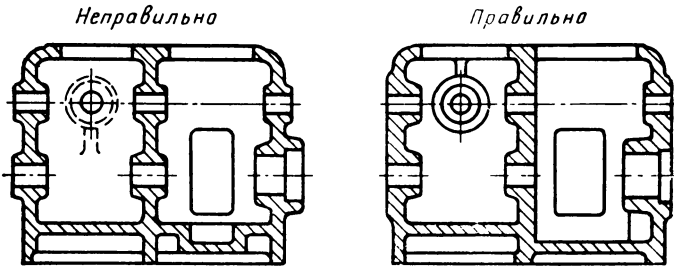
Пример неправильного и правильного оформления конструкции отливки, корпусной детали
